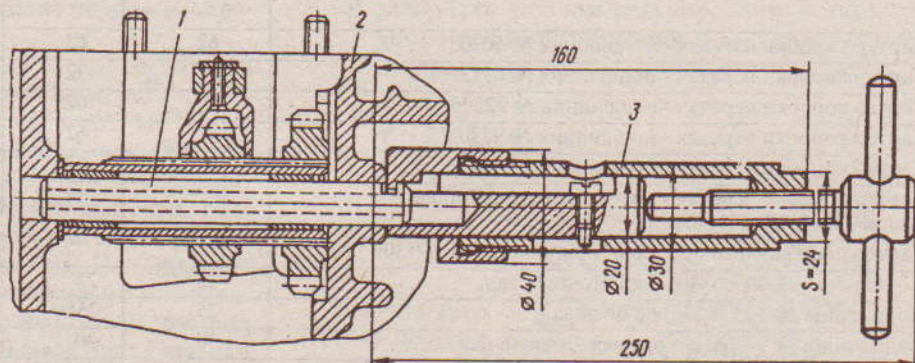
Съемник оси шлицевого вала: 1 - ось шлицевого вала; 2 - картер коробки передач; 3 - съемник
